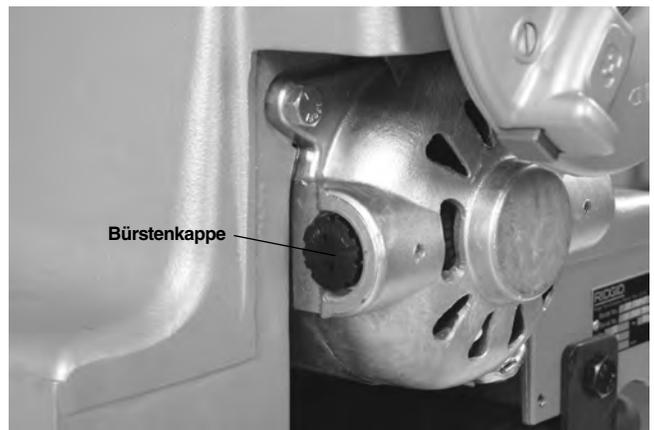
Entfernen der Motorabdeckung/Wechseln der Bürsten
